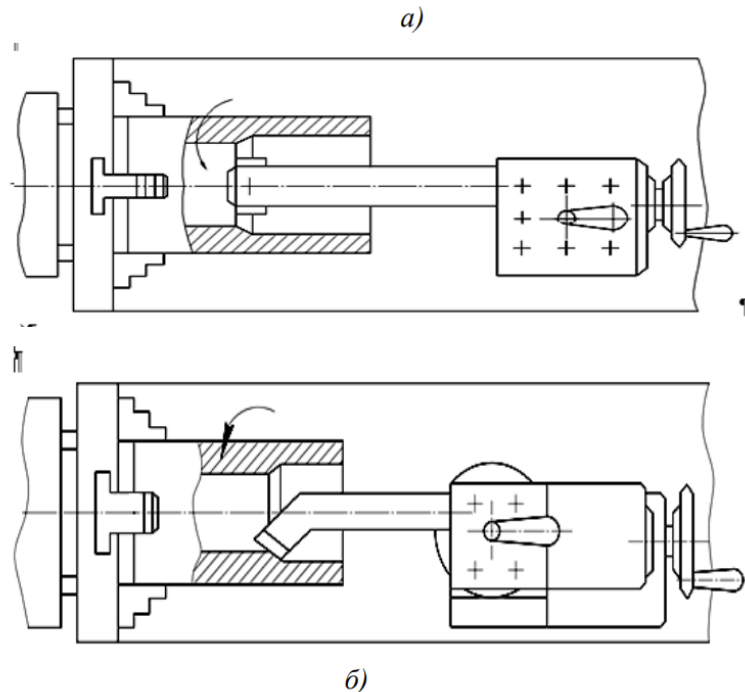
Схеми розточування на токарних верстатах: а – різцем, який закріплений в різцетримачі; б – різцем, який закріплений в консольній оправці
